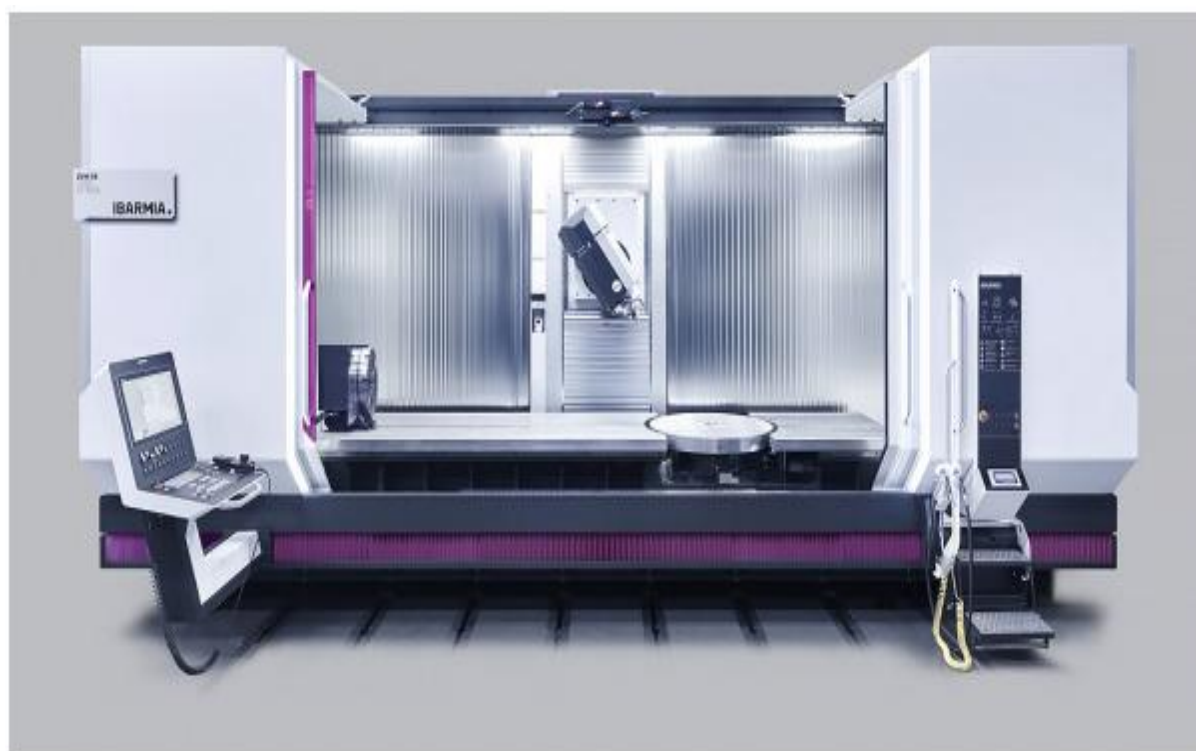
П'ятиосьовий обробний центр Ibarma ZVN EXTREME
